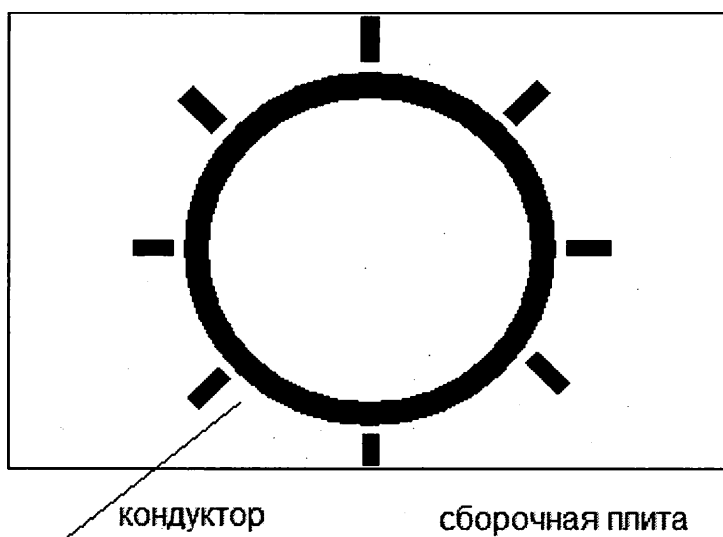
Кондуктор для сборки узла (обечайка 1 с упорами)
